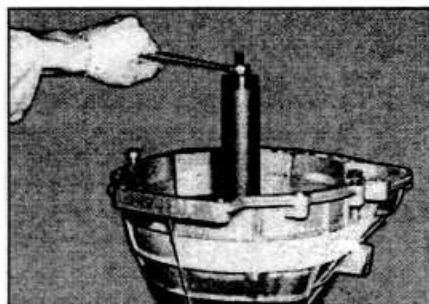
Соединение картера коробки передач с задней крышкой с помощью приспособления 16.041
